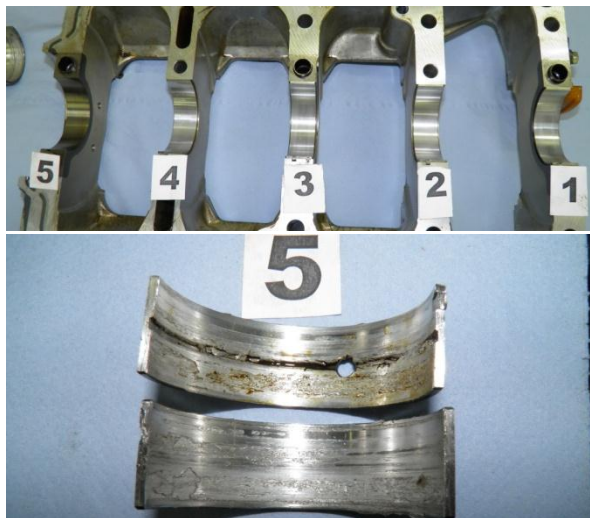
Пример конструктивно-производственного дефекта коренных подшипников коленвала, который привел к проворачиванию вкладыша и выходу ДВС из строя
